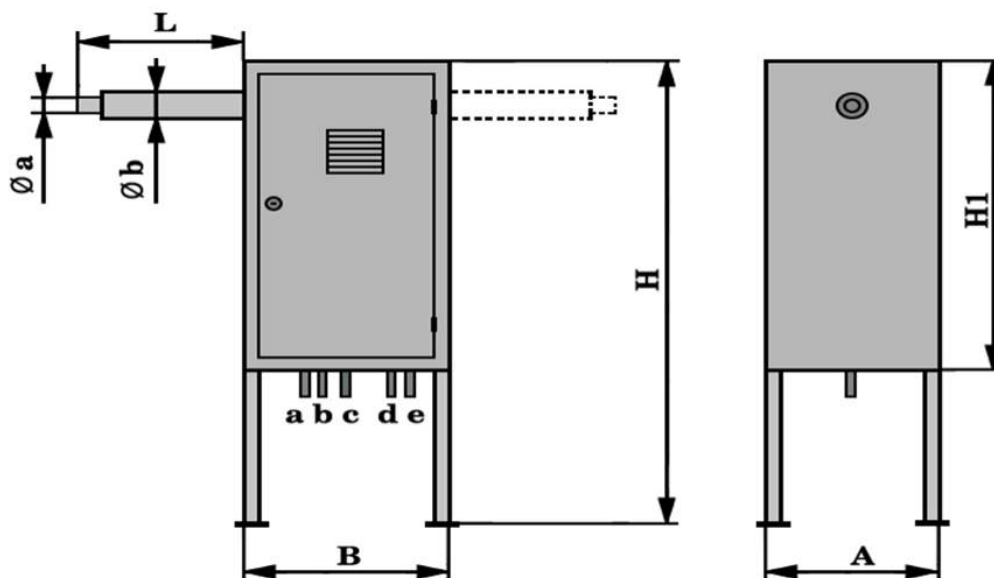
Габаритные размеры бокса для котлов наружного размещения
